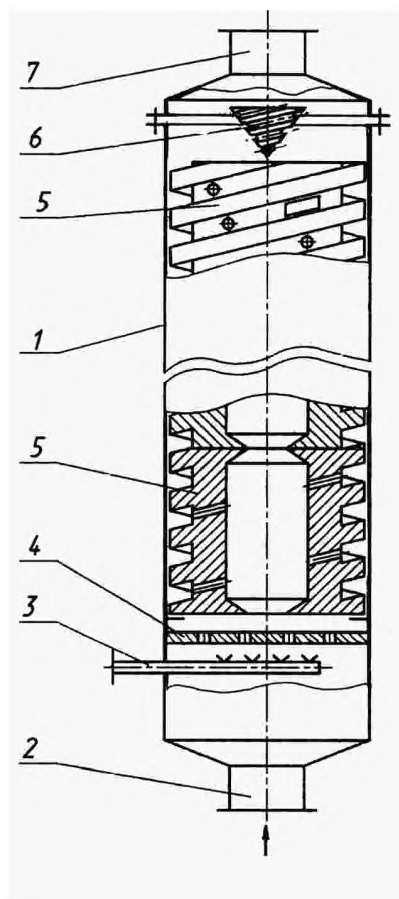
Общий вид трубчатого турбулентного реактора диффузор-конфузорной конструкции с насадками для хлорирования бутилкаучука: 1 — корпус аппарата; 2 — штуцер ввода раствора бутилкаучука; 3 — штуцер ввода газовой смеси или газа; 4 — рассекатель потока; 5 — насадки; 6 — статический смеситель; 7 — штуцер отвода газожидкостной смеси
